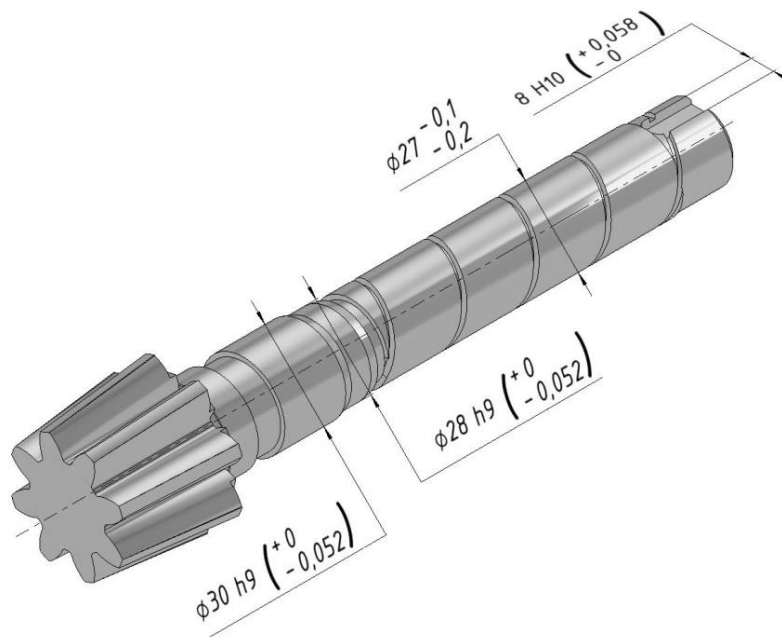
Рабочий чертеж вала-шестерни в изометрии С.КР 700-00-22 [Working drawing of pinion shaft in C.LV 700-00-22 isometry]
